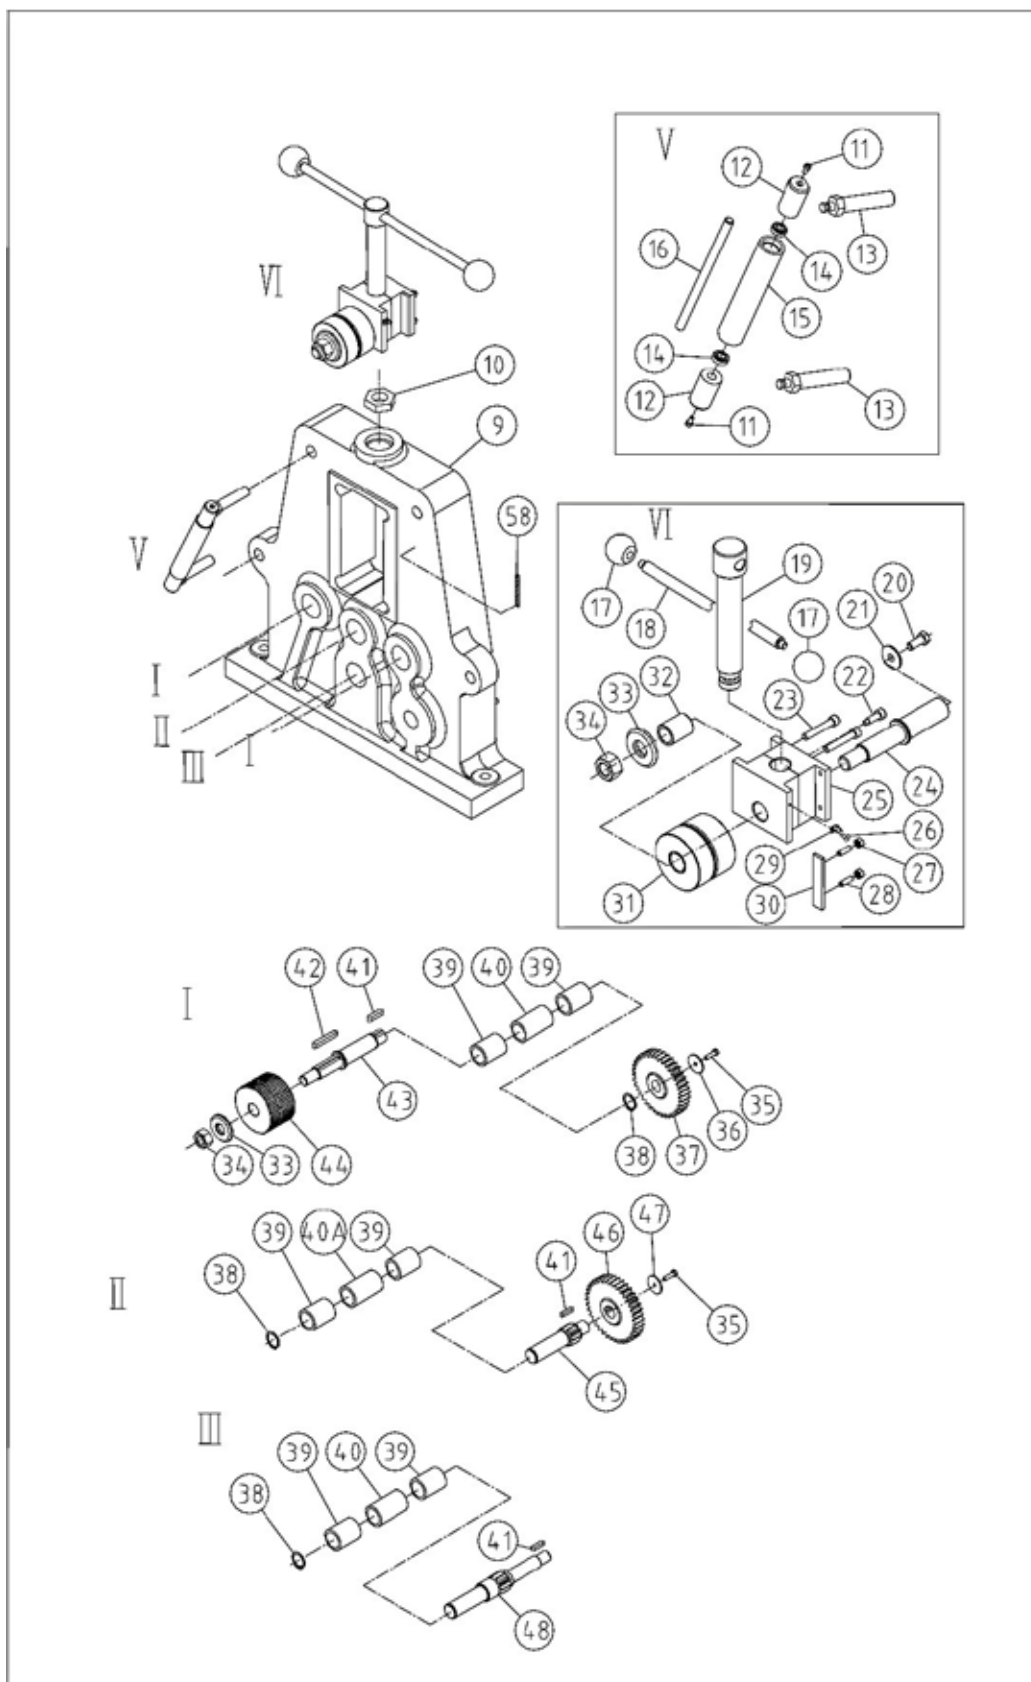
Vue éclatée 2 - PRM 10 E - Galets et pièces d'entraînement
